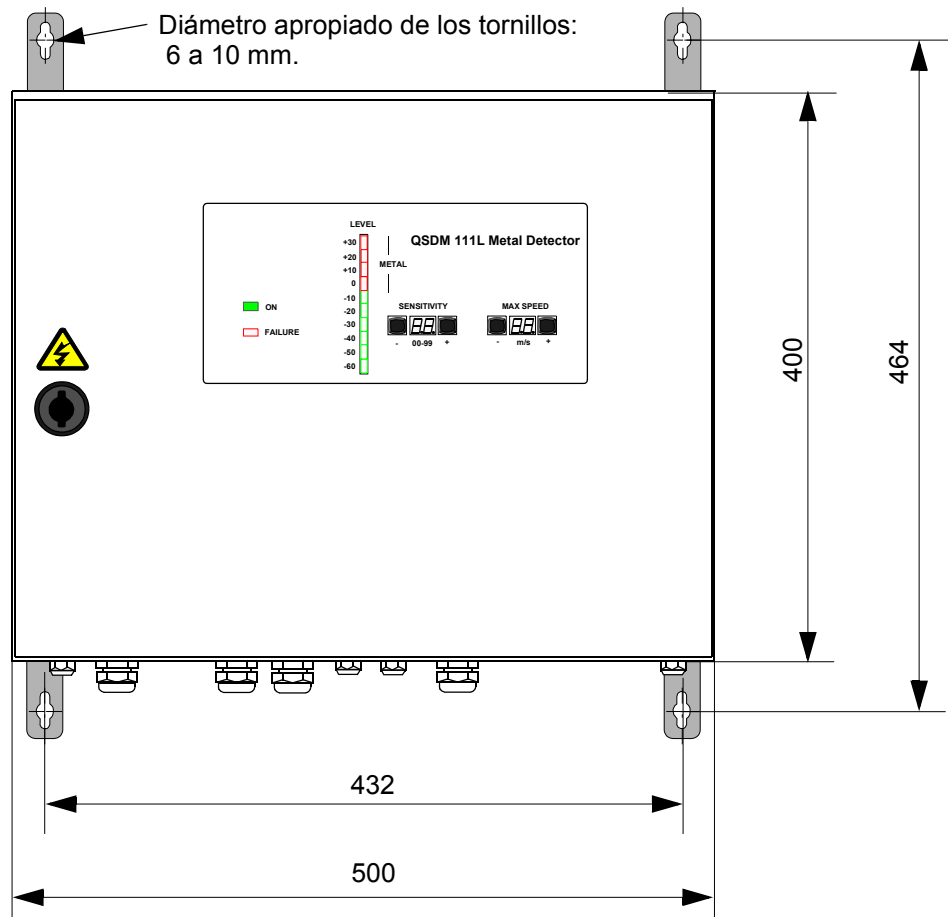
Plano de medidas y perforaciones para la unidad electrónica
